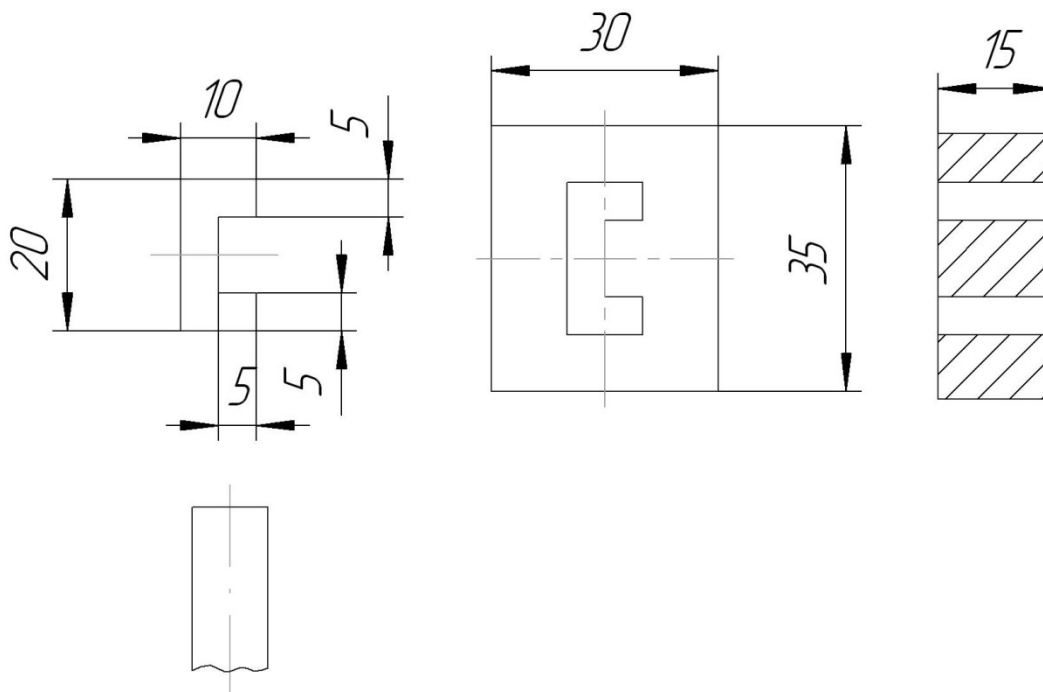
а) – эскиз инструмента; б) – эскиз заготовки.
